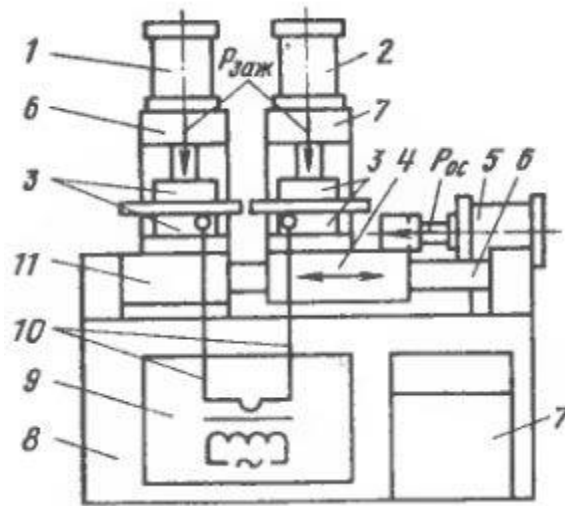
Схема машини для стикового контактеного зварювання
